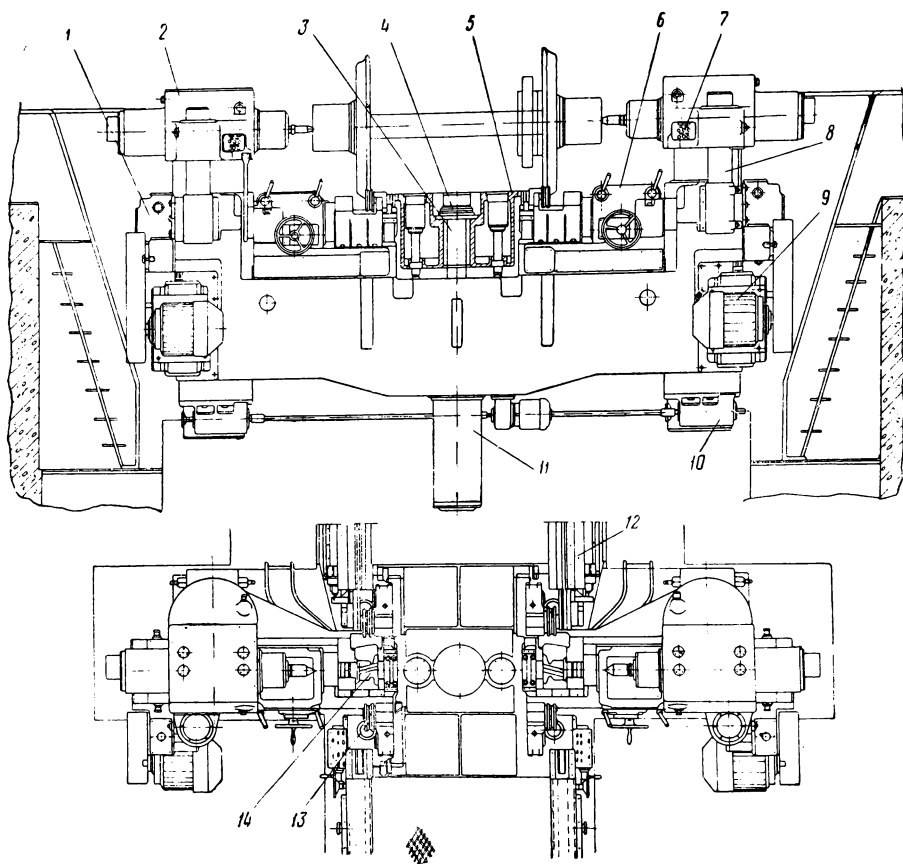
Общий вид фрезерного станка типа КЖ-20 для обточки бандажей колесных пар без выкатки:
